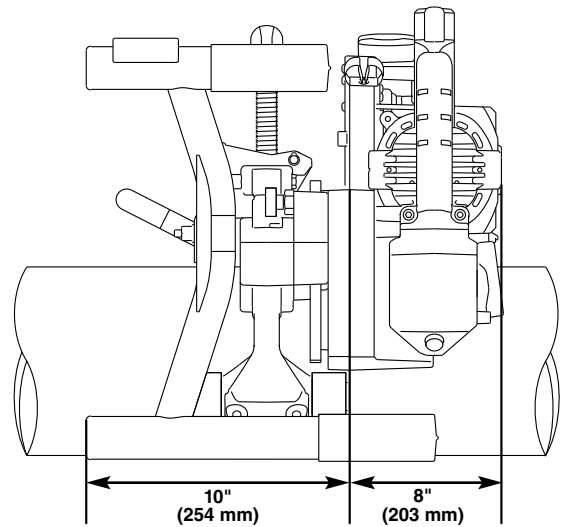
A – Encombrement axial de la PipeSaw sur tuyau
